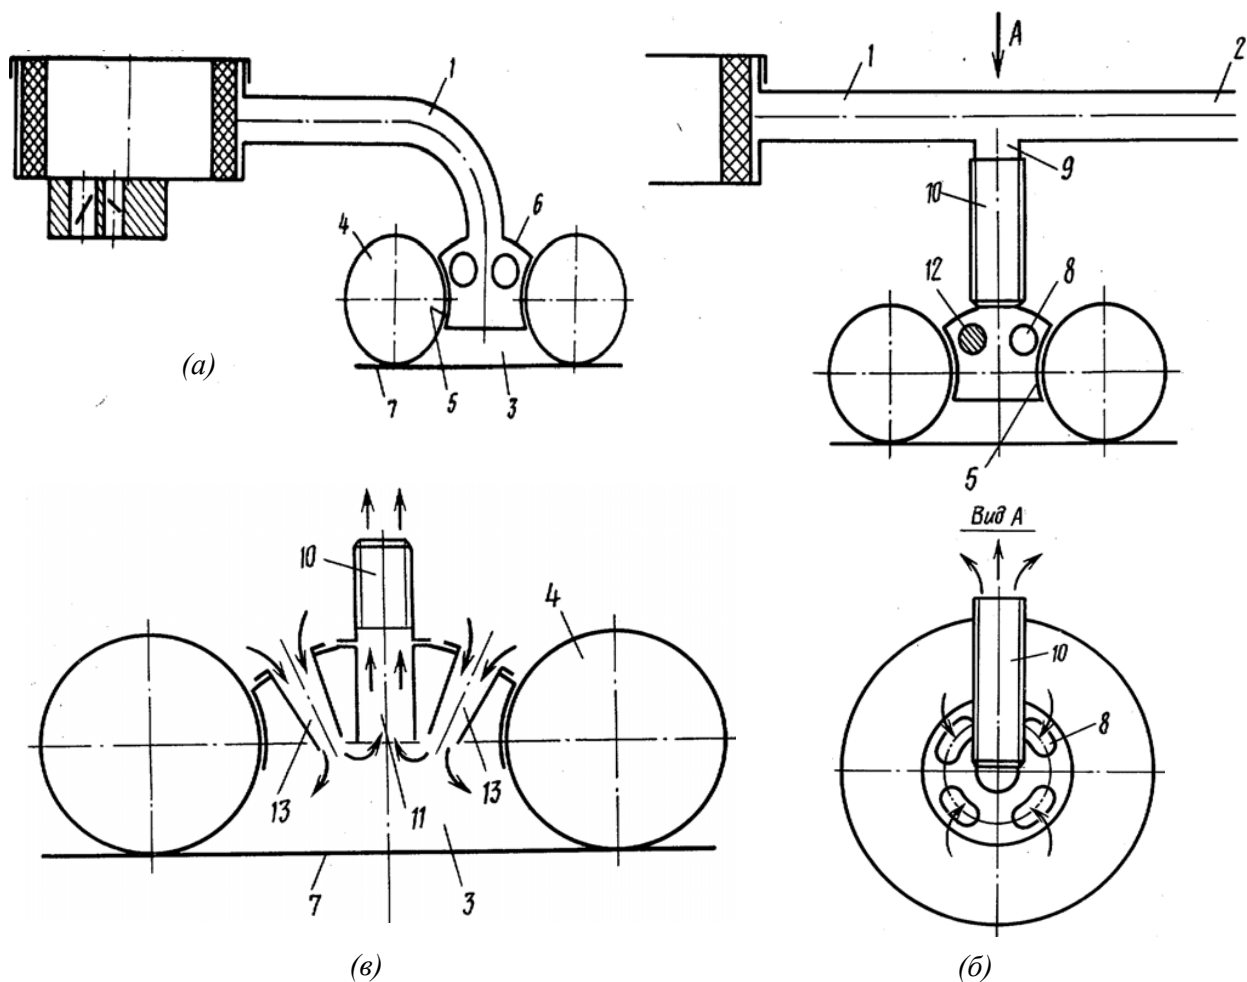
Схема глушителя шума системы впуска двигателя с последовательным (а) и параллельным (б) присоединением расширительной камеры, схема глушителя шума системы впуска двигателя с дополнительно установленными трубчатыми элементами (в):
